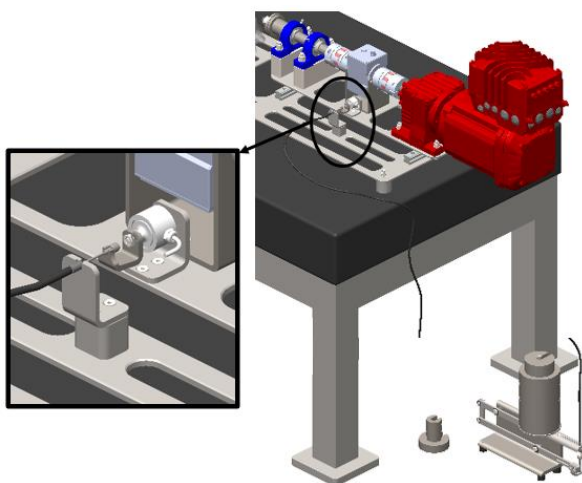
Montagem do cabo de aço do Conjunto 04 no Conjunto 02.
